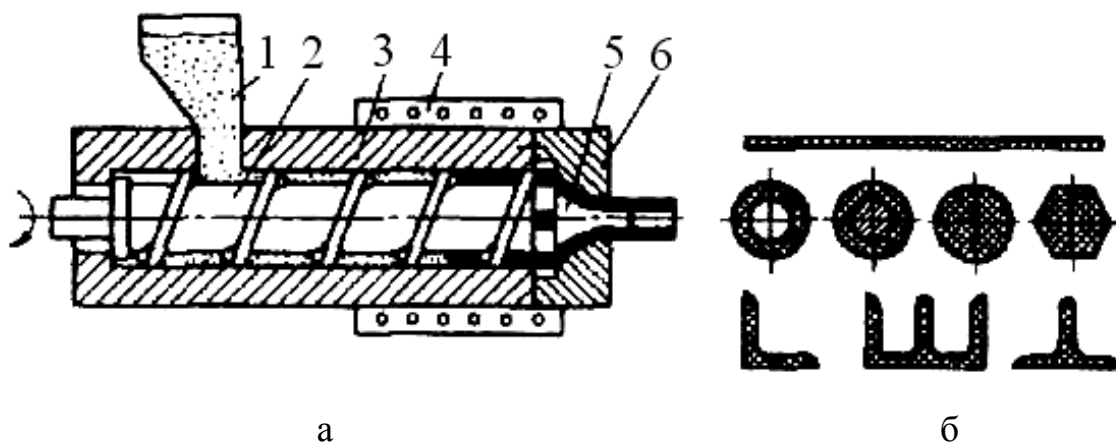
Непрерывное выдавливание: а - схема установки; б - профили получаемых деталей
